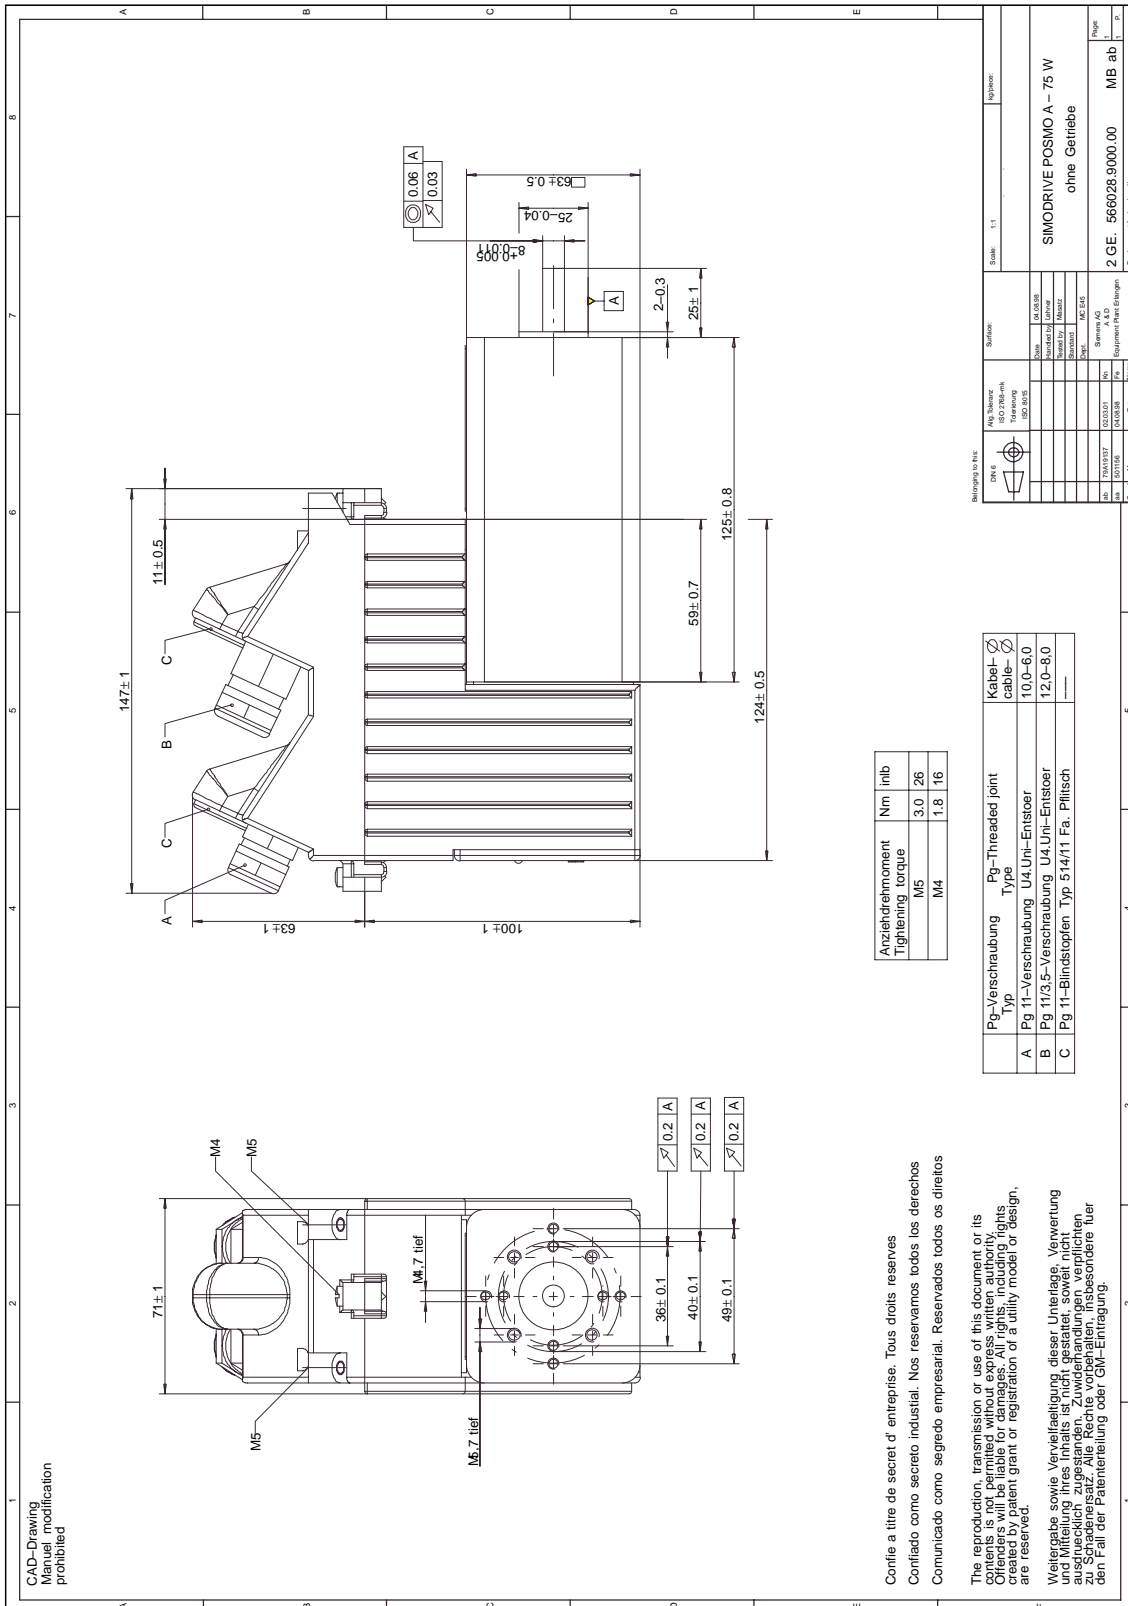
Maßblatt: SIMODRIVE POSMO A – 75 W ohne Getriebe
